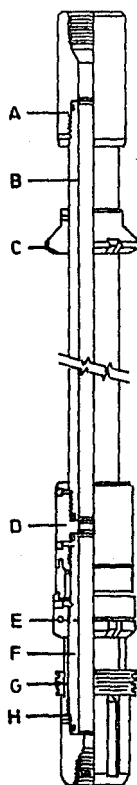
Herramienta soldadora tipo "C" (básica).
